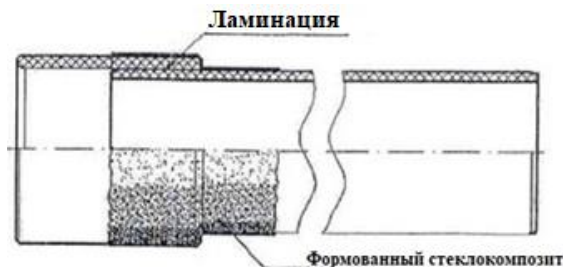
Поставка стеклокомпозитных труб с закрепленным раструбом из заготовки муфты без уплотнителей
